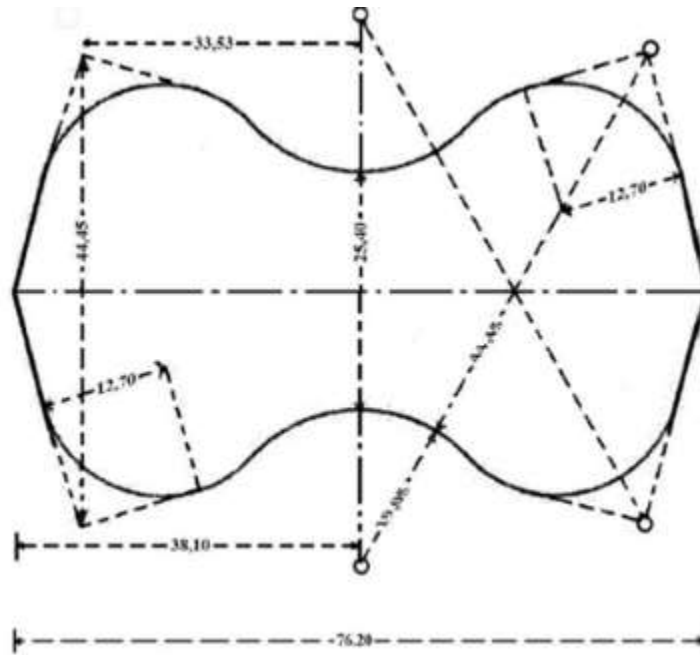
Dimensiones de espécimen para ensayo a la tracción.
